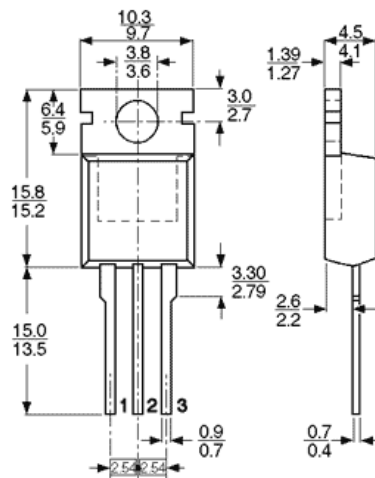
Габаритні розміри тиристора VTA06-600C
